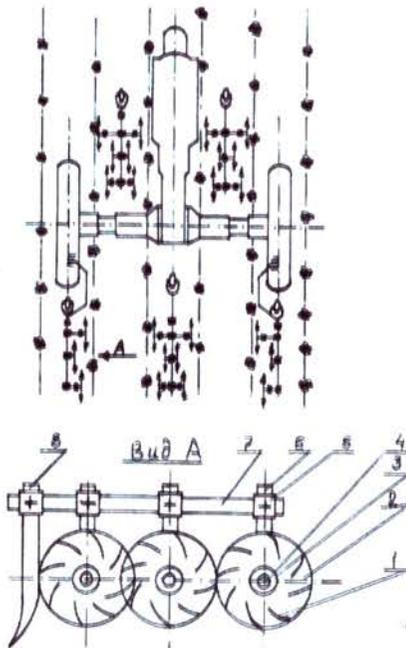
Шахматное расположение рабочих органов для разрушения почвенной корки и рыхления середины междурядья:
